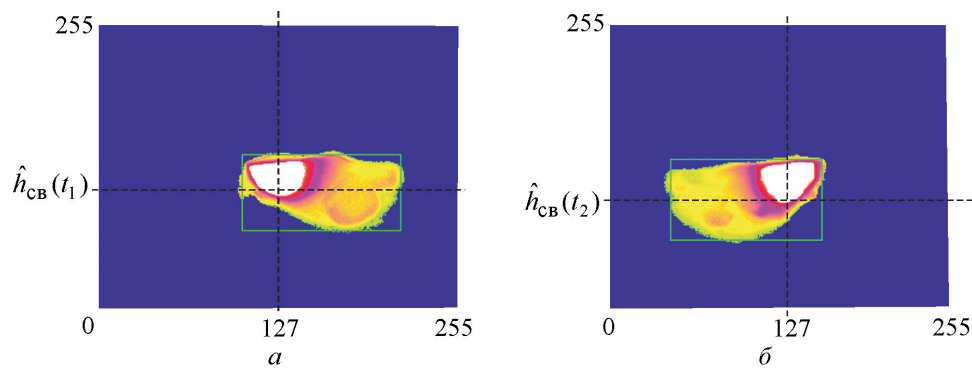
Изображение теплового поля сварочной ванны при сварке корневого шва с поперечными колебаниями в крайнем левом (а) и крайнем правом (б) положении относительно оси стыка
